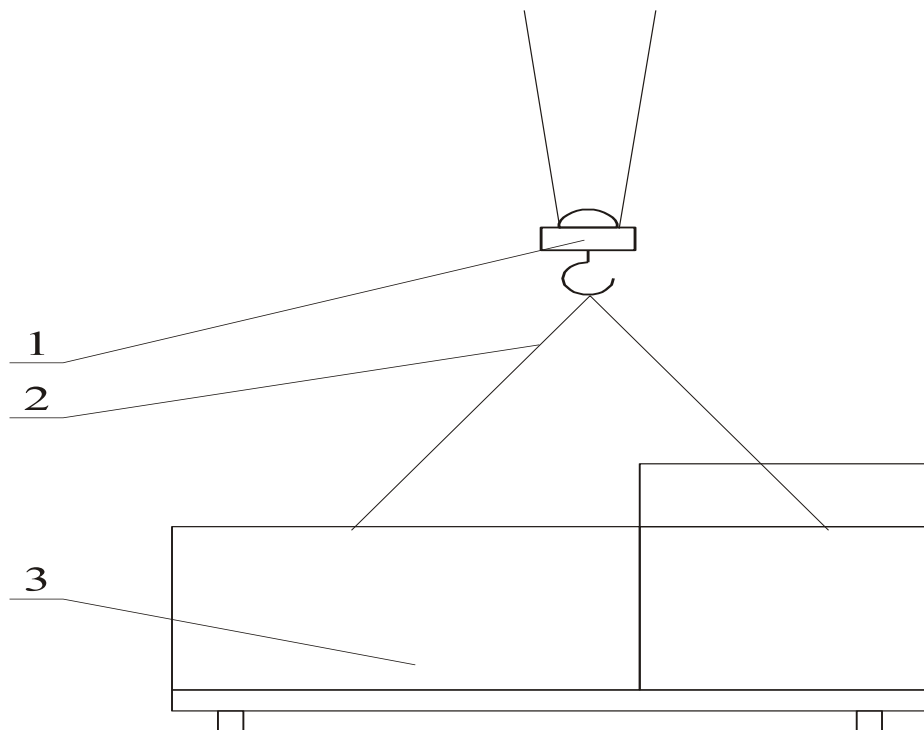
Схема строповки маслoutворювача-вотатора марки МСО-100
